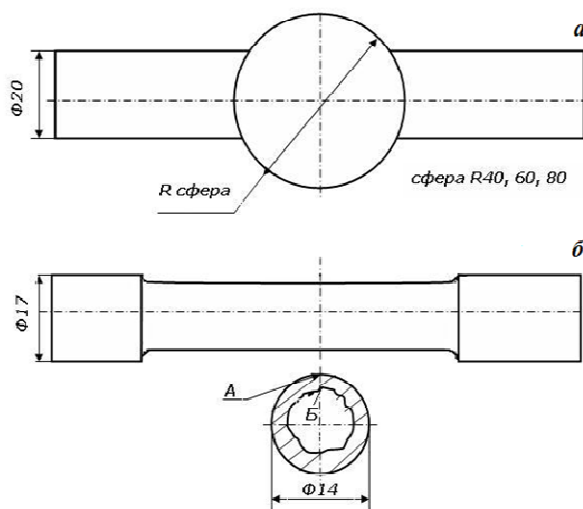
а) вид заготовки с искусственным дефектом, б) образец для испытаний на выносливость
